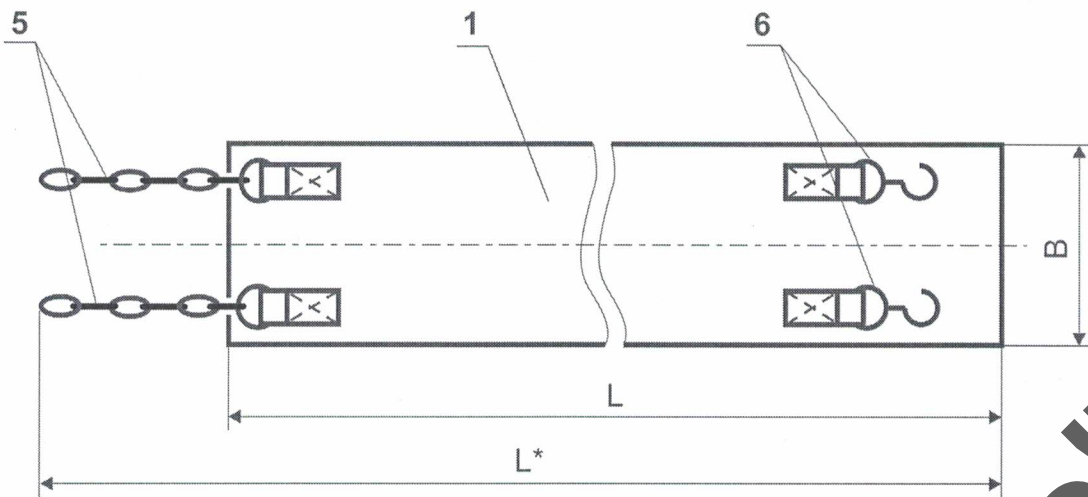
Теплоизоляционный пояс универсальный (ТПУ)
